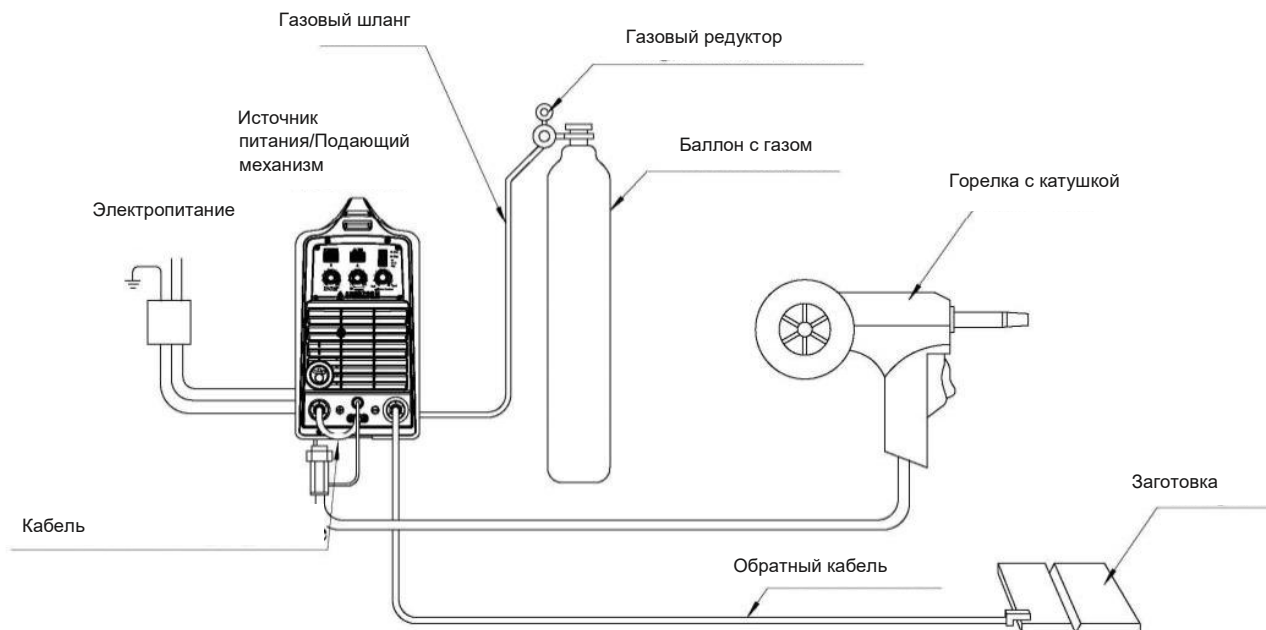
MIG/MAG сварка алюминиевой, алюминиево-магниево проволокой с помощью катушечной горелки
